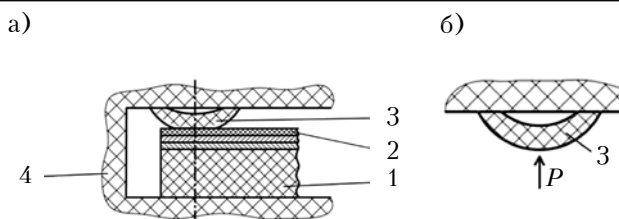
Конструкция разъемного соединителя в сборе (а) и фрагмент вкладыша до сборки (б): 1 — жесткая печатная плата; 2 — ГПК; 3 — вкладыш; 4 — корпус соединителя
